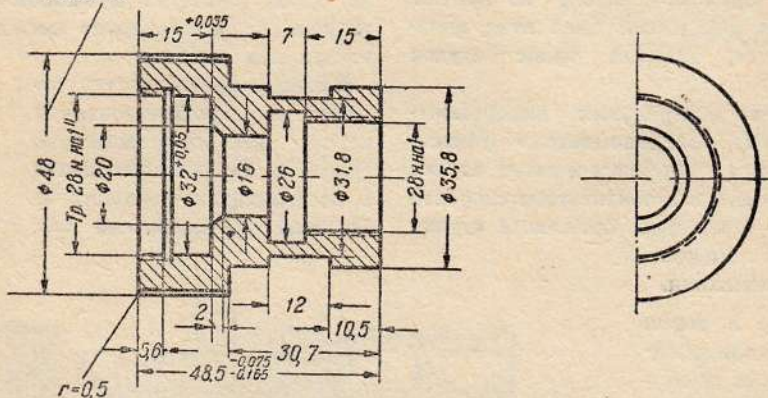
Втулка для шарикоподшипника вала барабана, ближайшего к маховику
